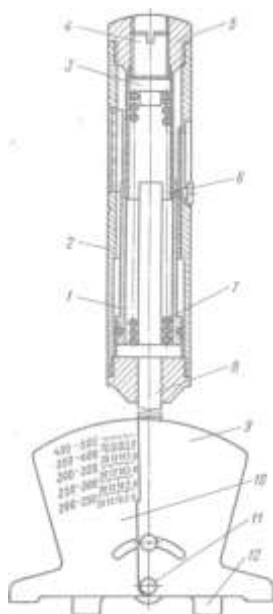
Устройство КИ-8920 для проверки натяжения ремней привода вентилятора, генератора, компрессора
